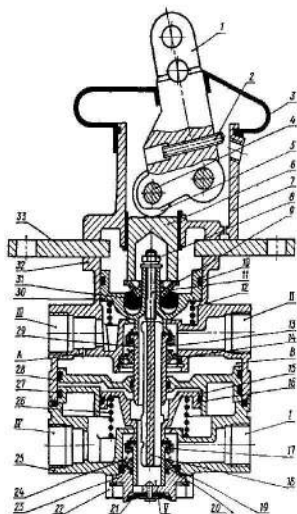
Кран тормозной двухсекционный с рычагом: 1 - рычаг; 2 - упорный винт рычага; 3 - защитный чехол; 4 - ось ролика; 5 - крючок; 6 - толкатель; 7 - корпус рычага; 8 - гайка; 9 - тарелка; 10, 16, 19, 27 - уплотнительные кольца; 11 - шпилька; 12 - пружина следящего поршня; 13, 24 - пружины клапанов; 14, 20 - тарелки пружин; 15 - поршень малый; 17 - клапан; 18 - толкатель; 21 - атмосферный клапан; 22 - упорное кольцо; 23 - корпус атмосферного клапана; 25 - нижний корпус; 26 - пружина верхнего поршня; 28 - большой поршень; 29 - клапан верхней секции; 30 - следящий поршень; 31 - упругий элемент; 32 - верхний корпус; 33 - опорная плита; I...IV - выводы
